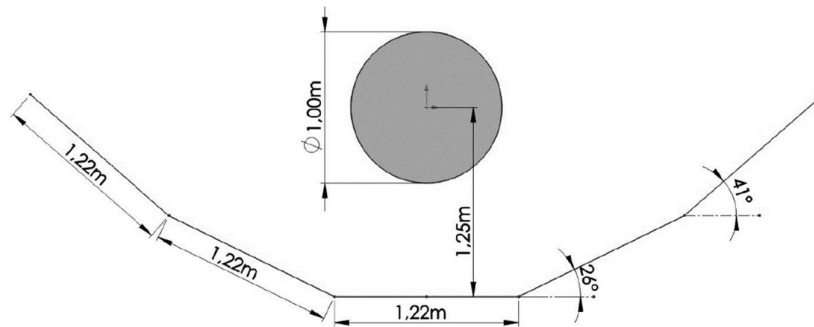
Diseño de Estructura Parvati. Fuente (Autor)
